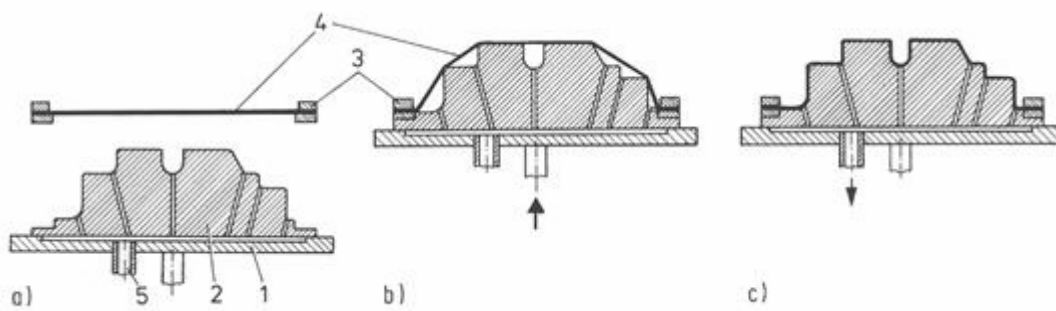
Mechanické tvarování – pružný tvárník[vlastní zpracování]
